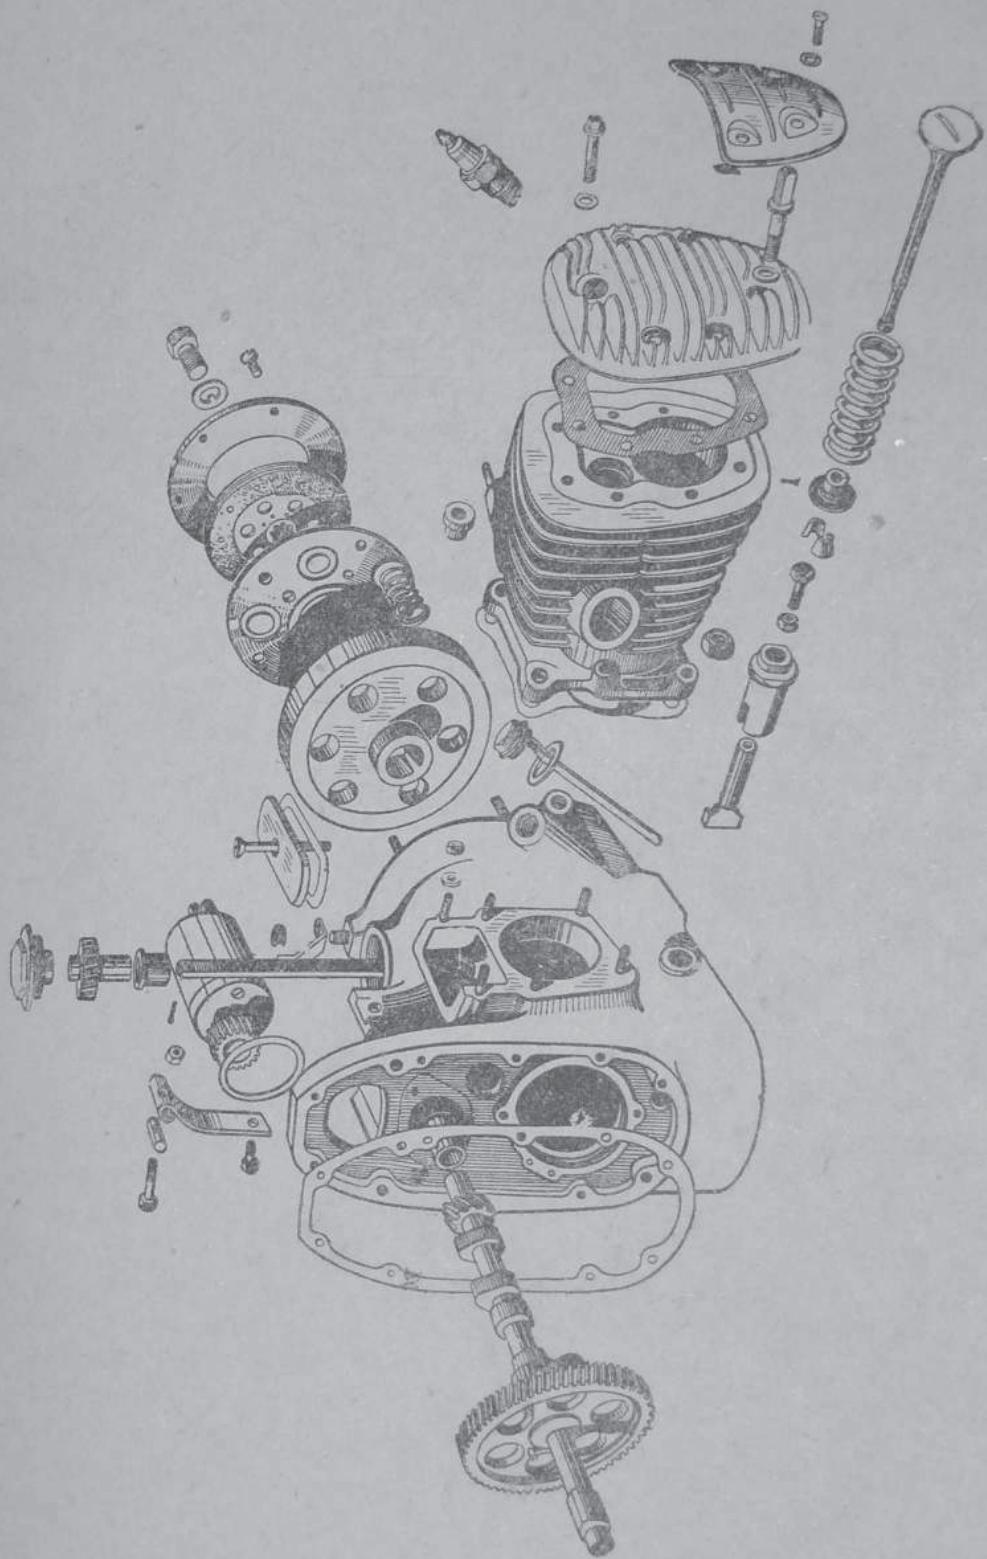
Распределительный механизм верхнеклапанного двигателя.
